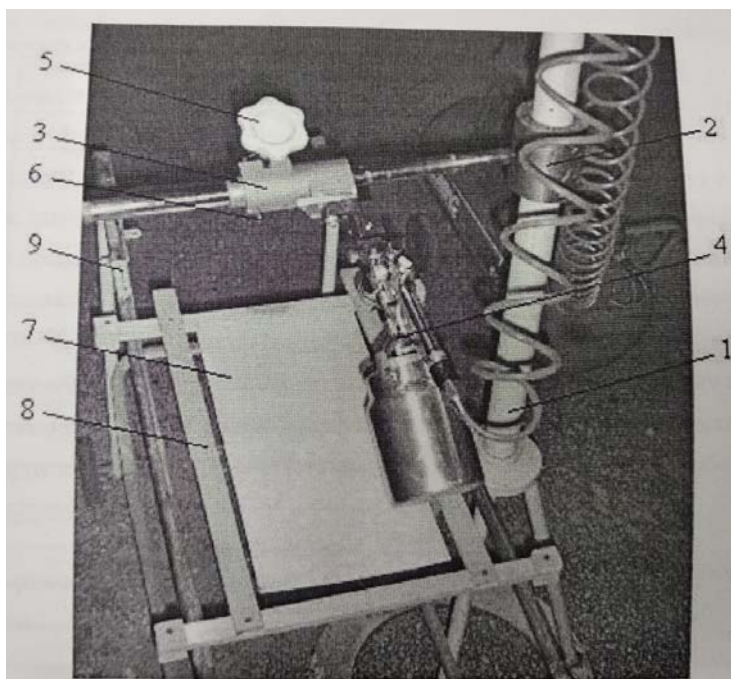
Установка для нанесения упрочняющего покрытия на заготовку заполнителя
